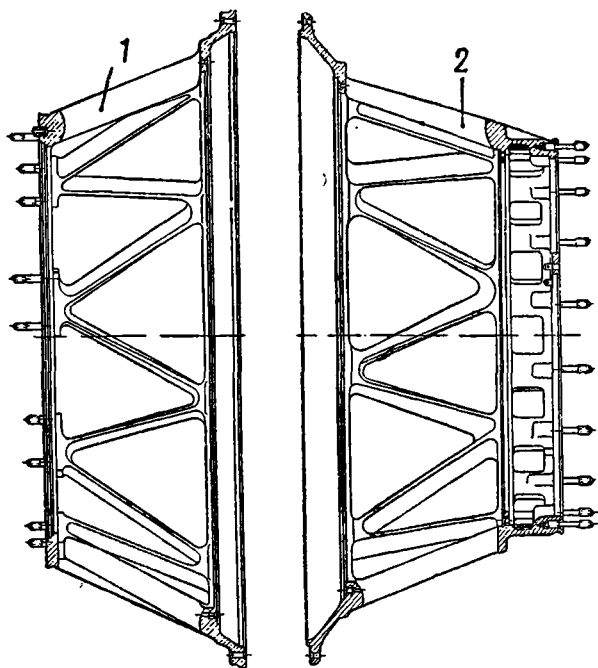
17. Корпус компрессора двигателя ВК-1.
